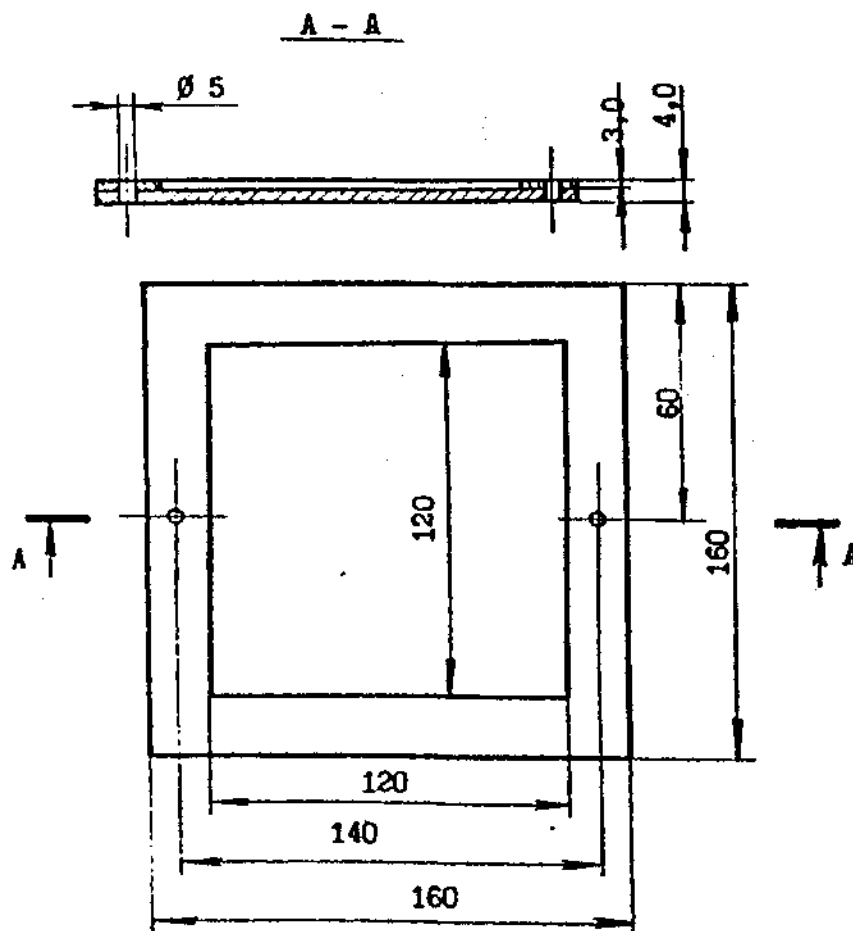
Форма для приготовления образцов-пластин из рабочего состава мастики
